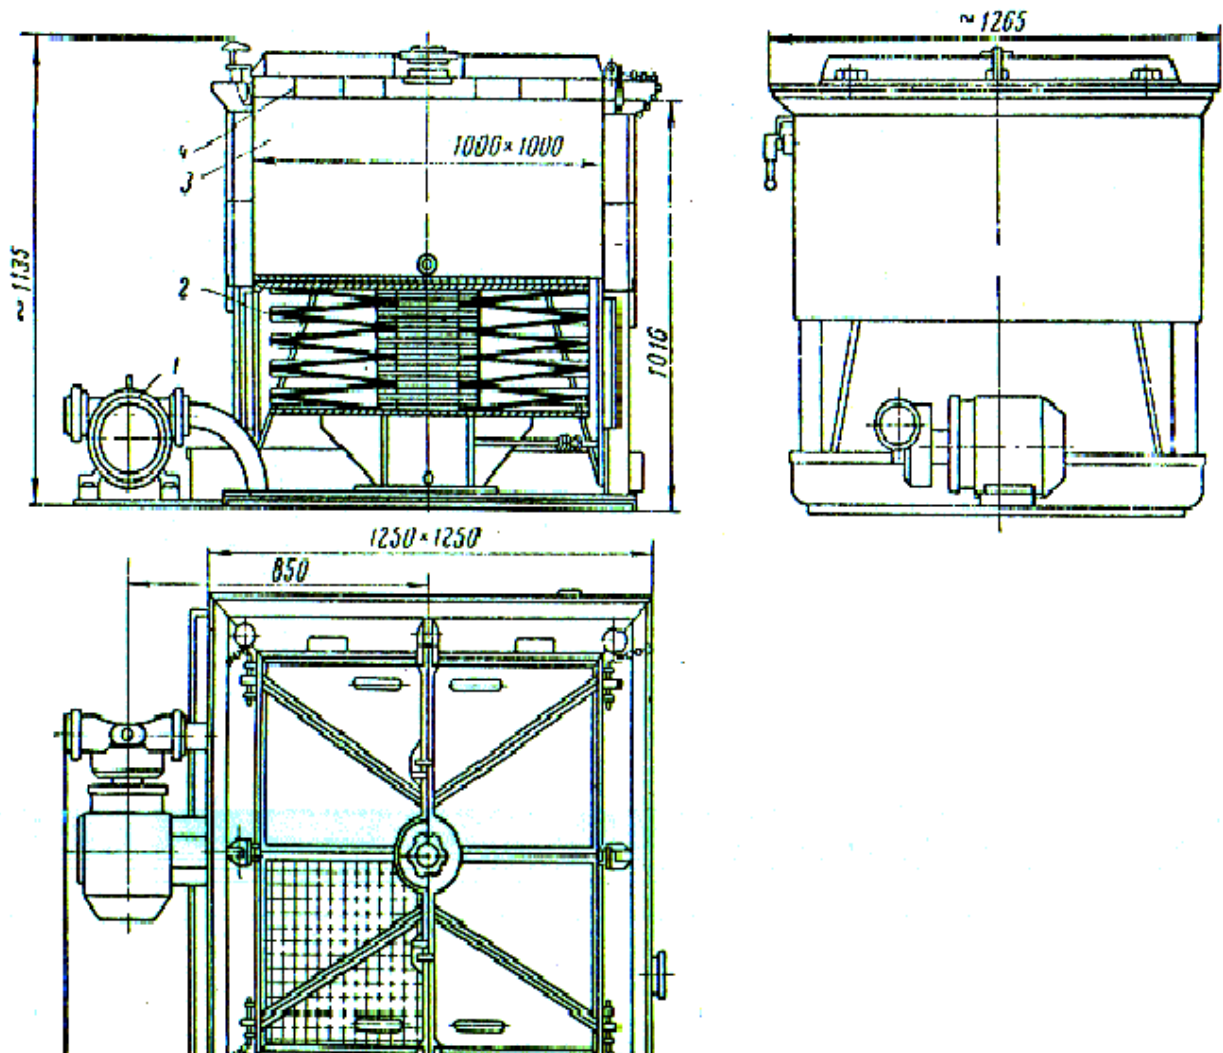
Формовочний апарат П – 738 – В з сифонним приводом
